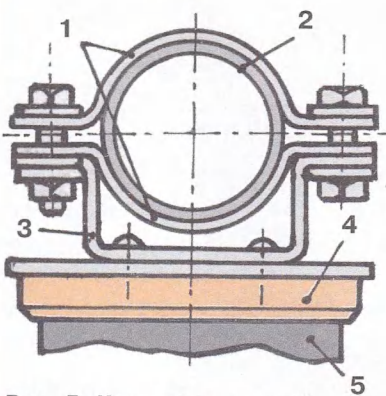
Крепление частей штанги соединителем: 1 – скобы; 2 – штанга; 3 – соединитель; 4 – шайба розетки; 5 – розетка.
